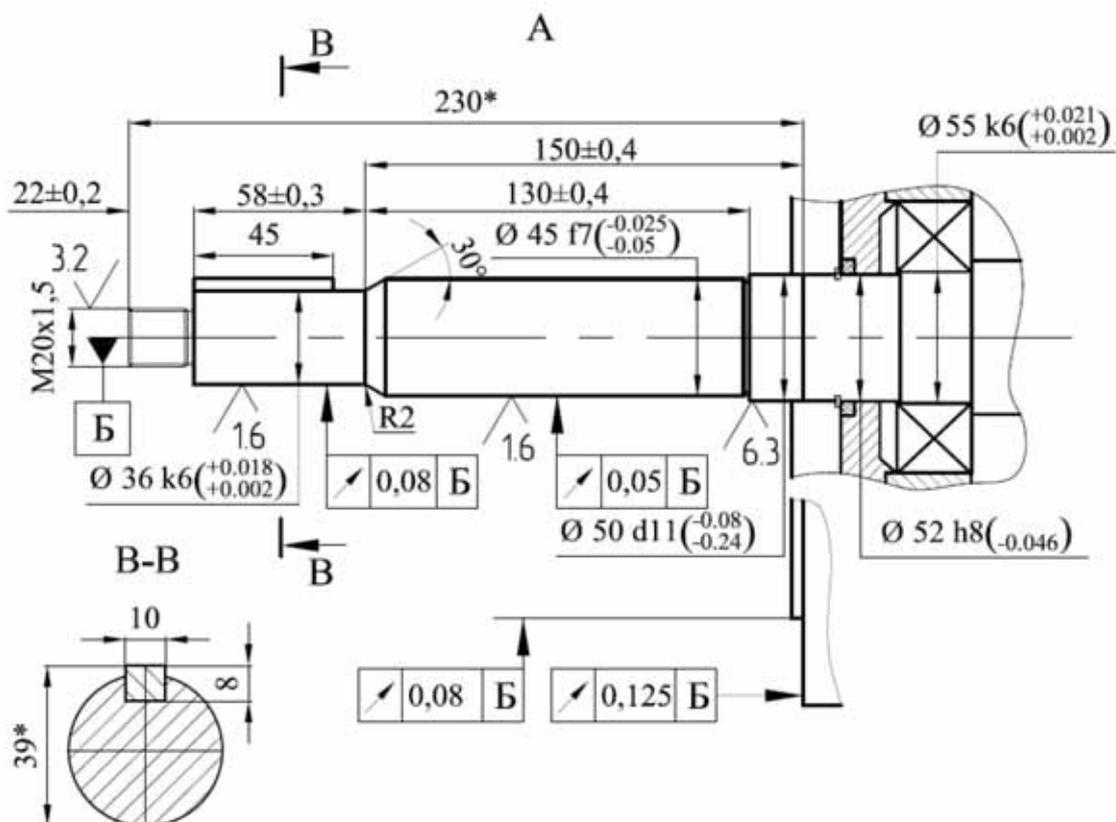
Свободный конец вала двигателя 6АМУ160М4ЖУ2, 6АМУ160М6ЖУ2
